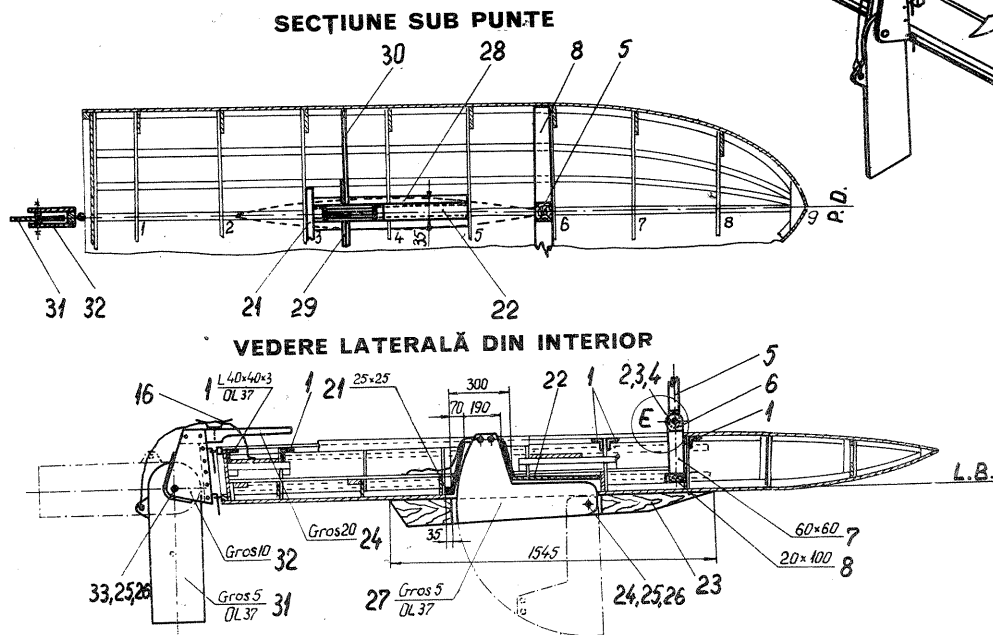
a — PLAN GENERAL DE CONSTRUCȚIE
